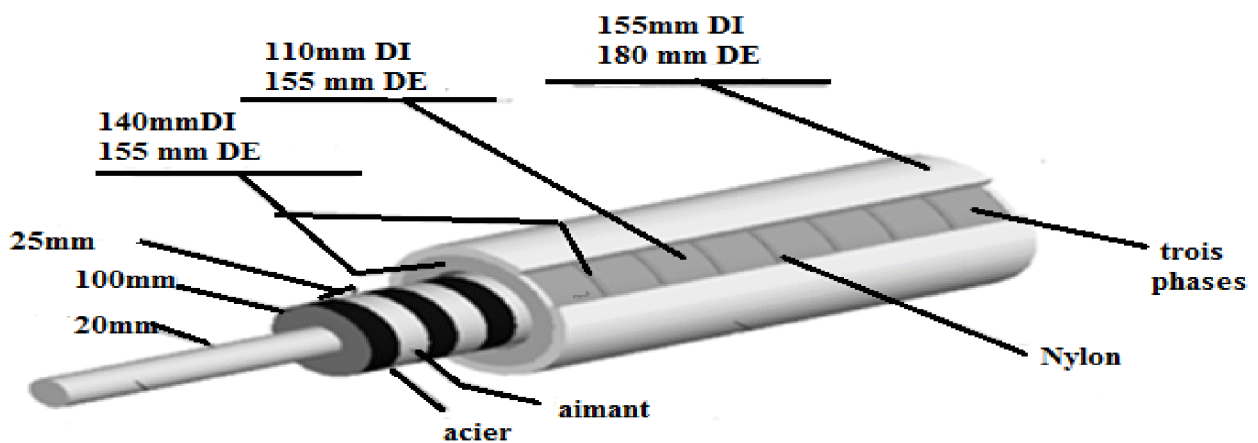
Dimensions d'une machine tubulaire (3KW) [2].
